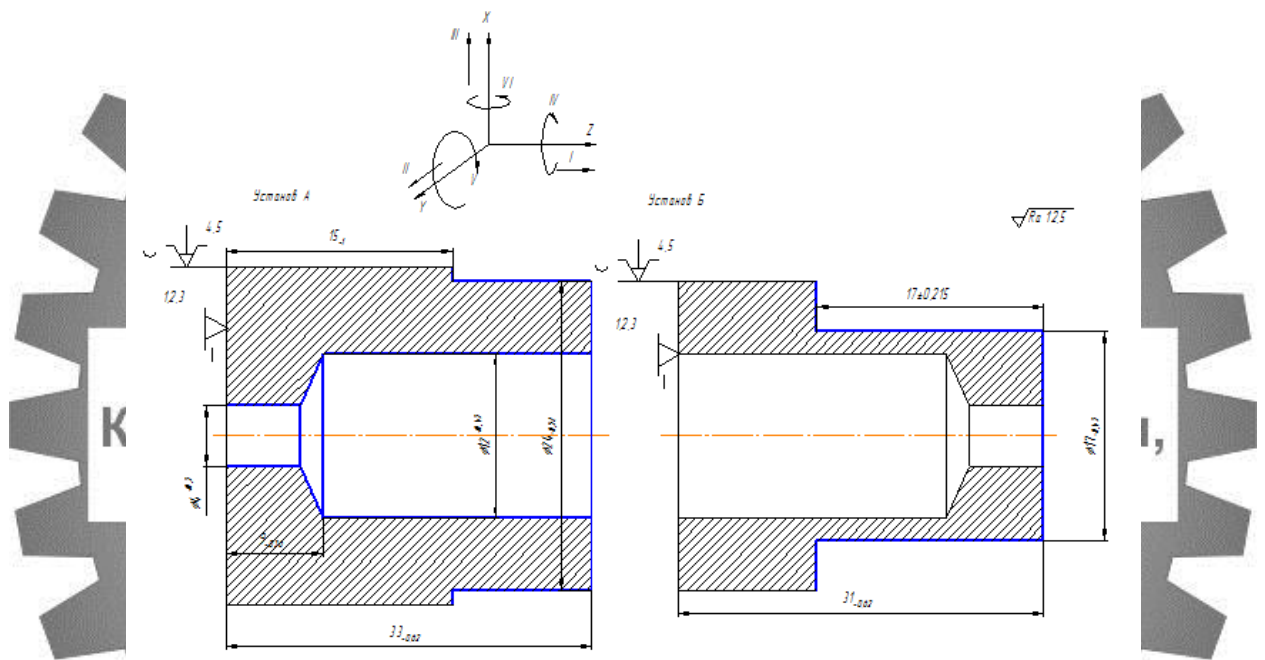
Схема базування заготовки ковпачка вивідного на операції
